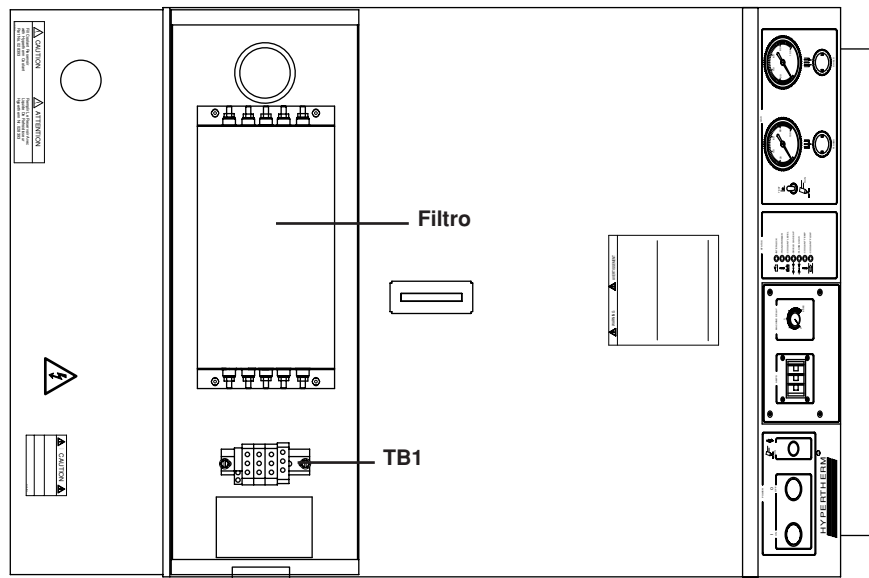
Fuente de alimentación MAX200 con la cubierta del filtro EMI retirada – Vista desde arriba
